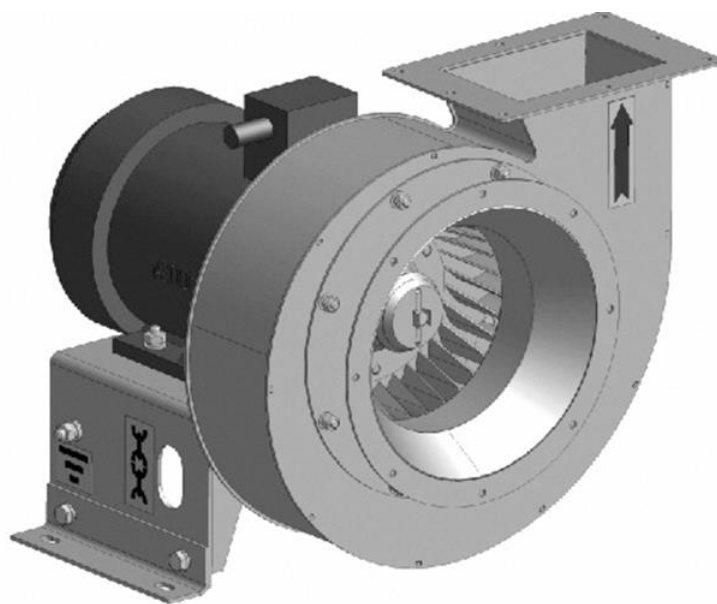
Загальний вид димососа сушильного барабана
